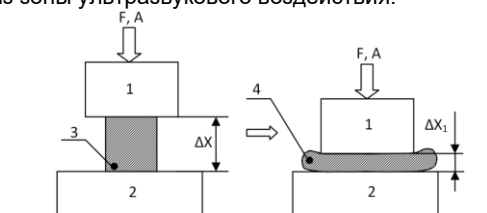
Схема воздействия УЗ колебаний на полимерный образец
